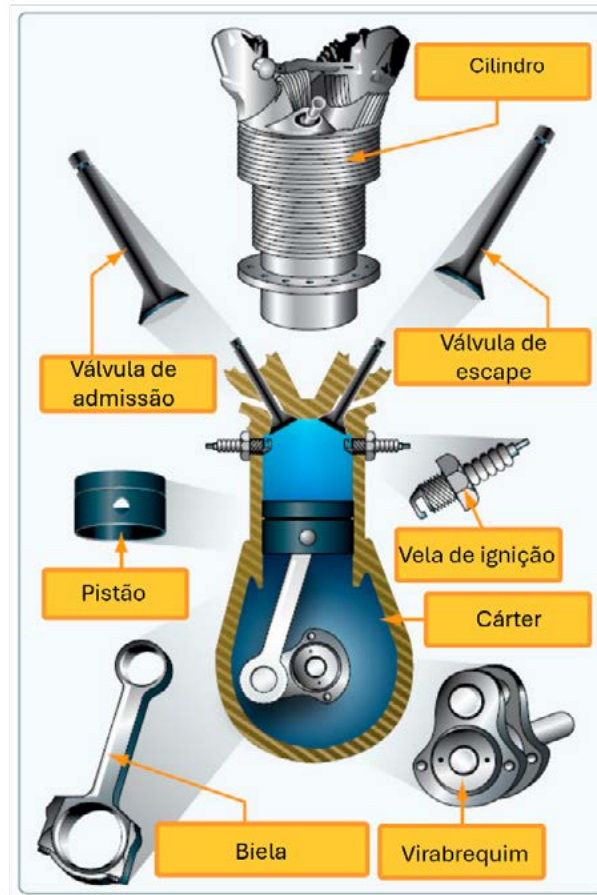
Principais componentes de um motor alternativo de ignição por centelha.
